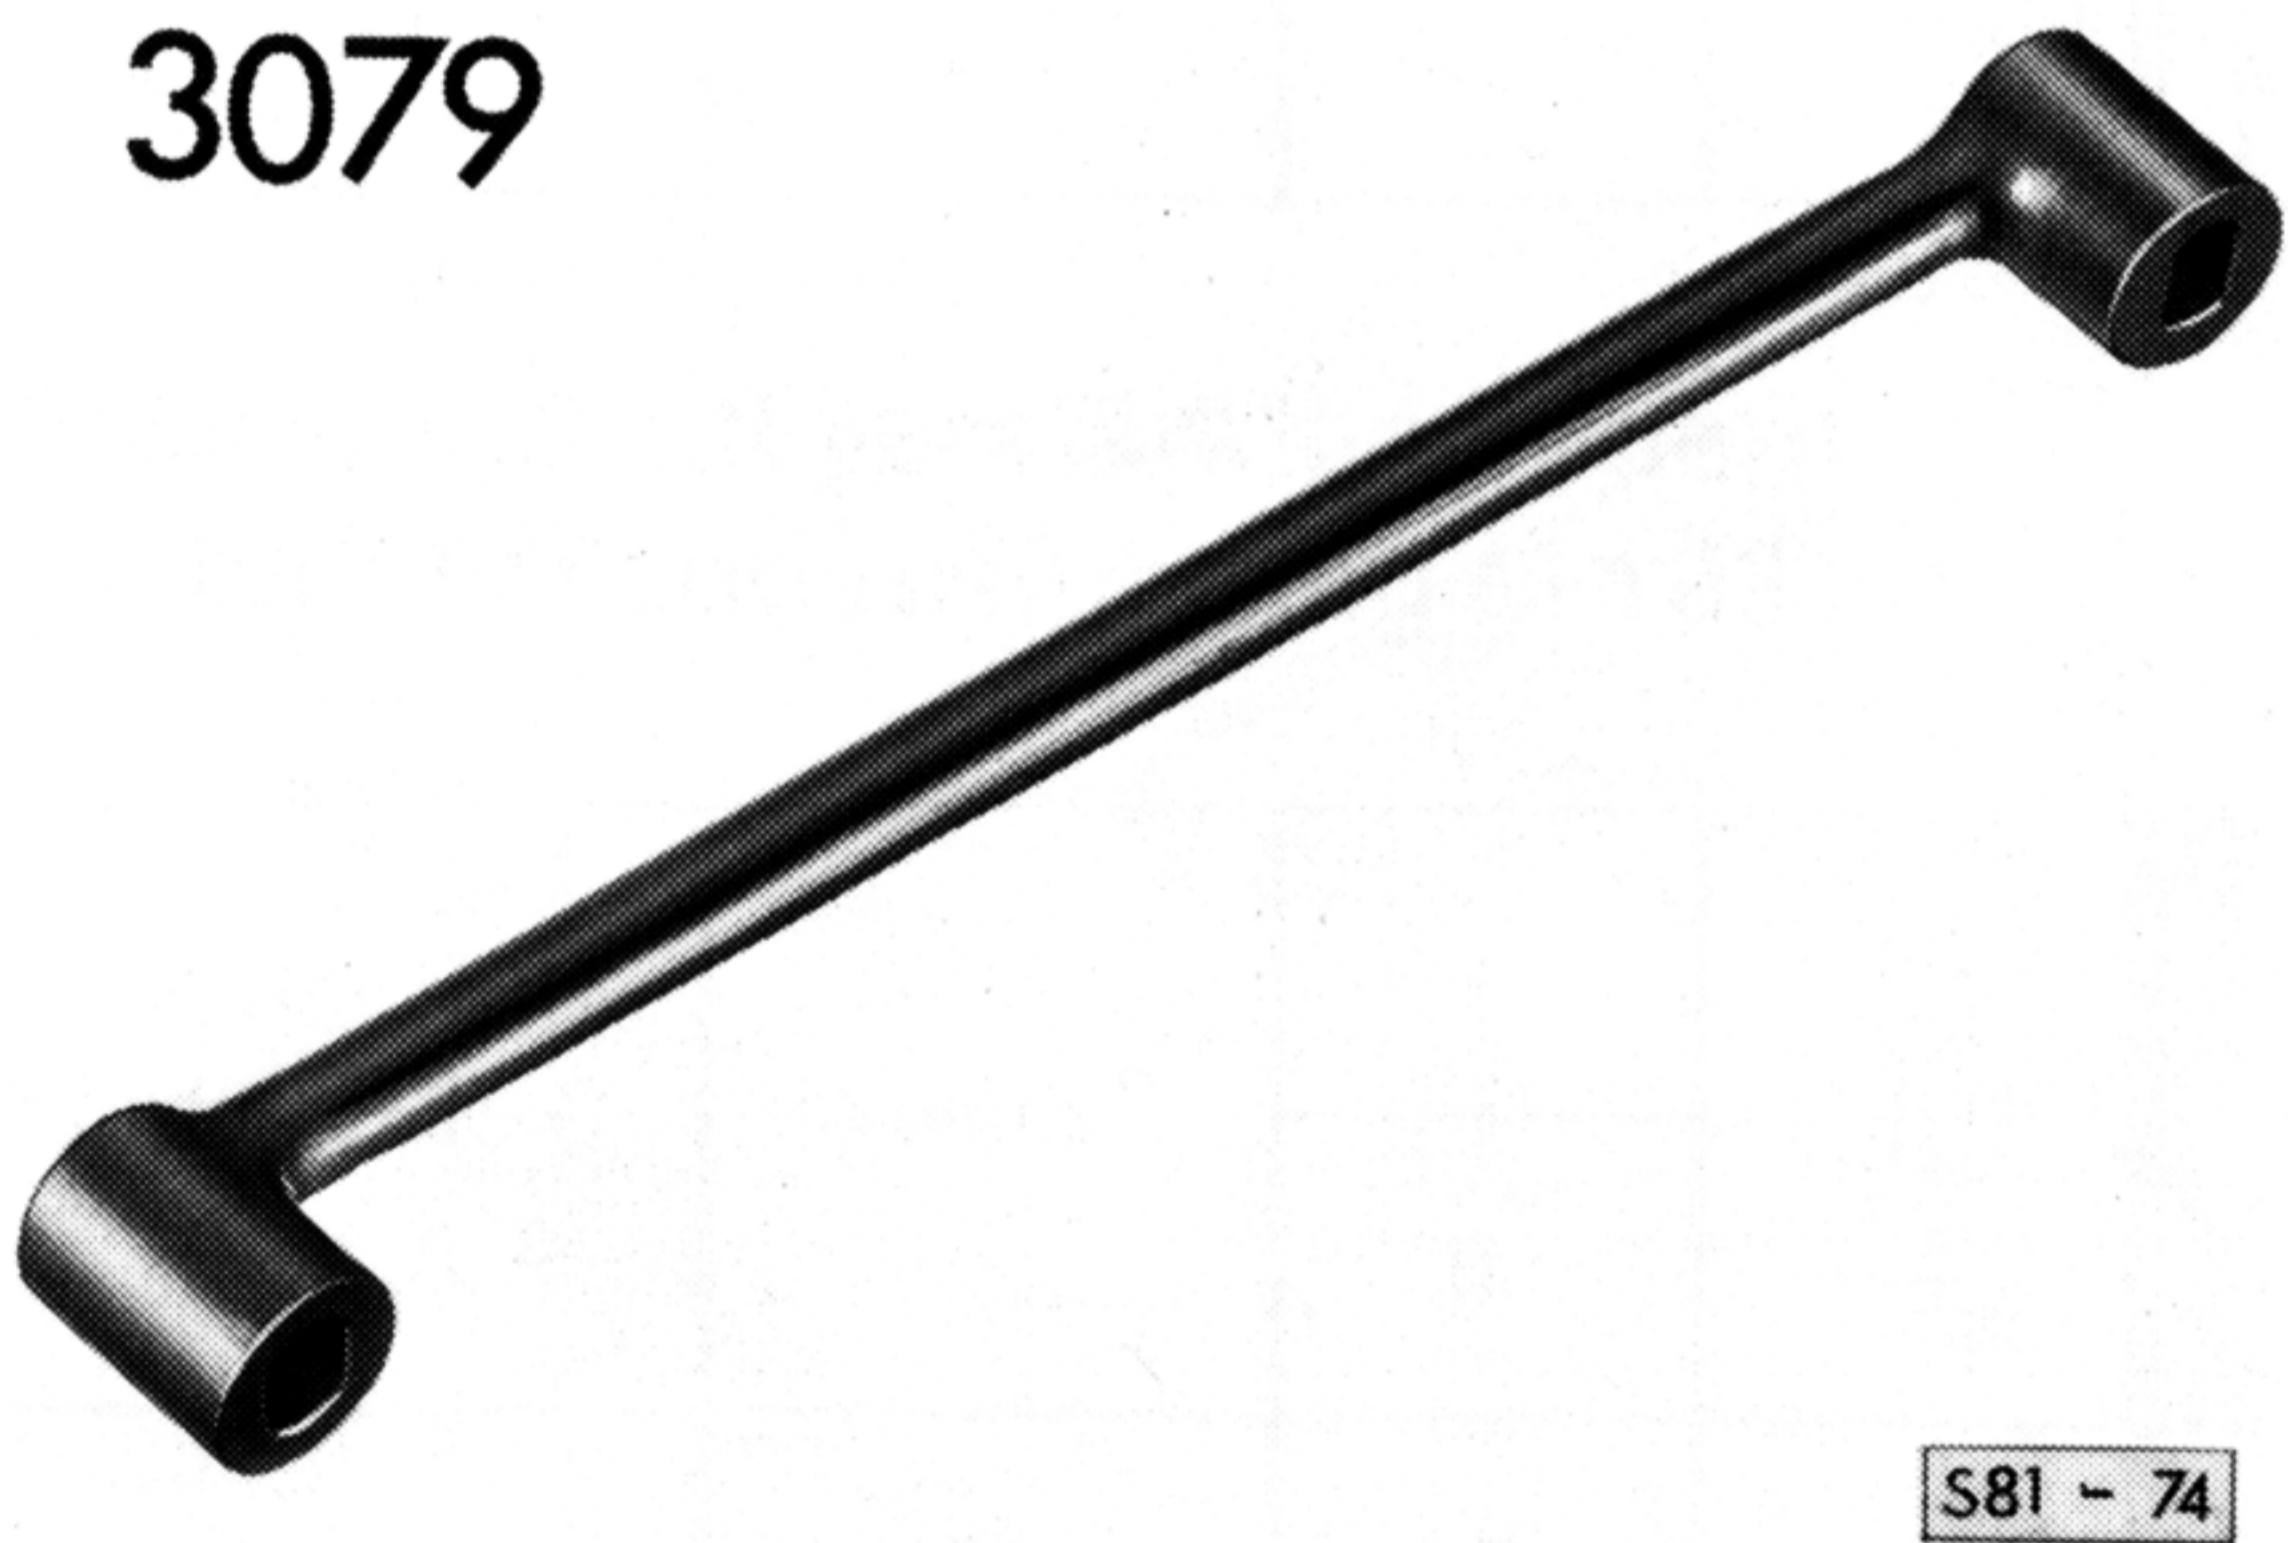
Sonderwerkzeug 3079 zum Gegenhalten beim Ausbauen des Dämpfers
